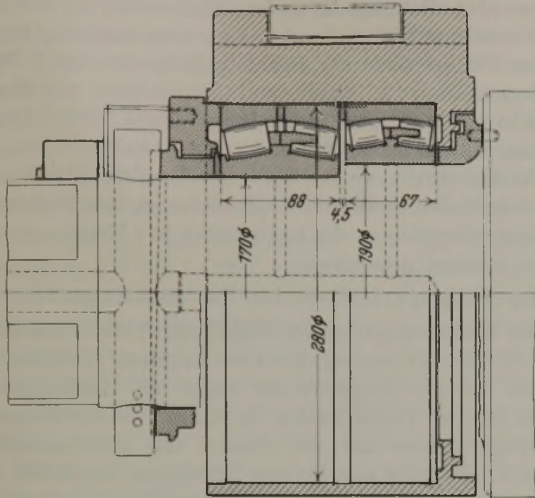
Rollenlager für Axial- und Radialdruck.
